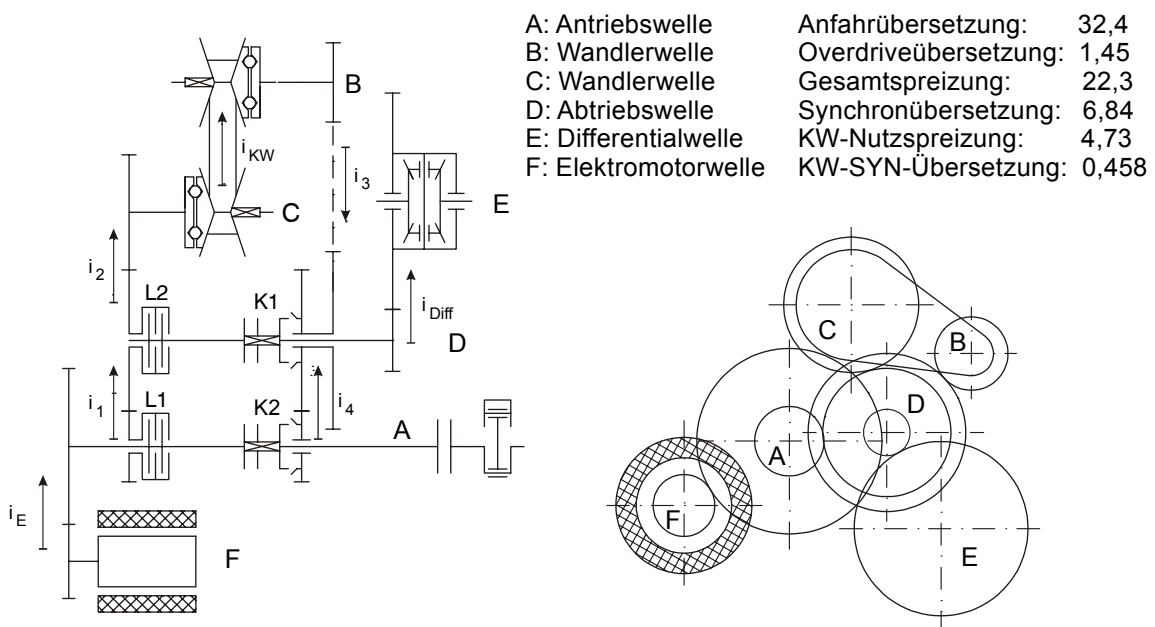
Verwirklichtes i^2 -Getriebe mit Seitenansicht
